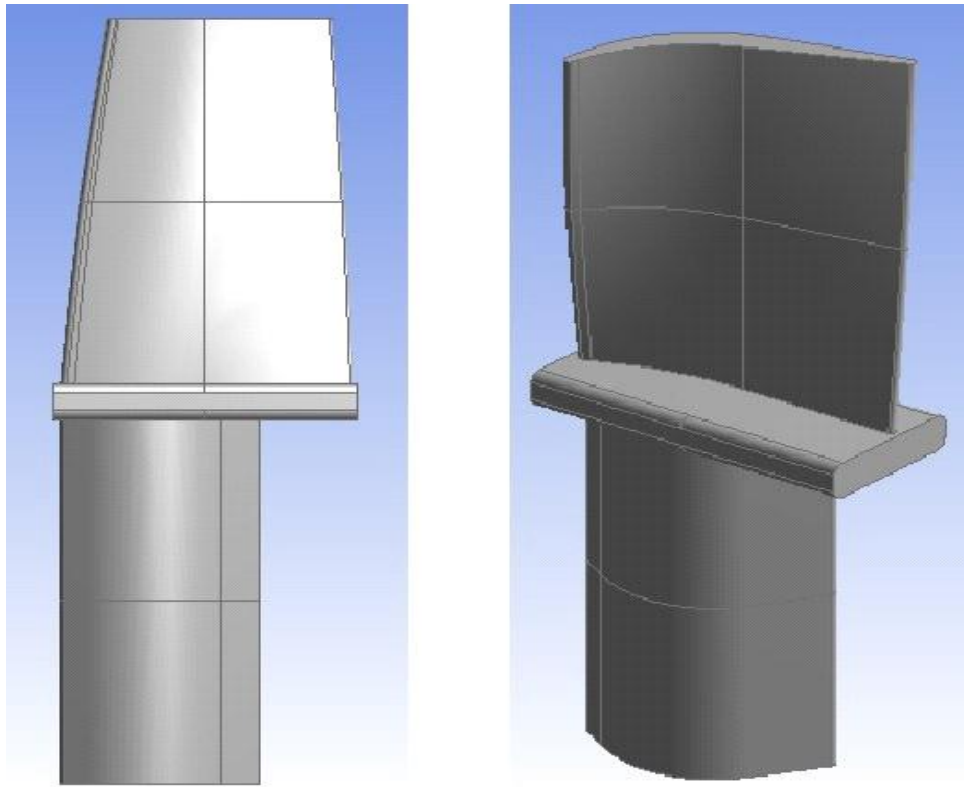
Параметрична CAD-модель двох'ярусної лопатки
